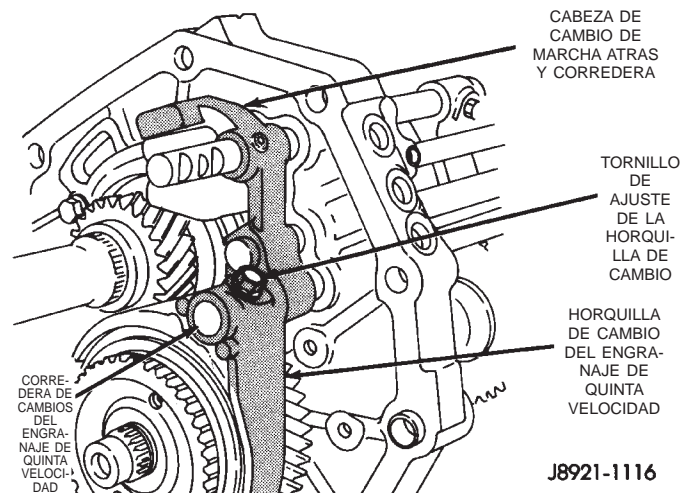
Instalación de perno de retén de horquilla de cambio de engranaje de quinta velocidad
